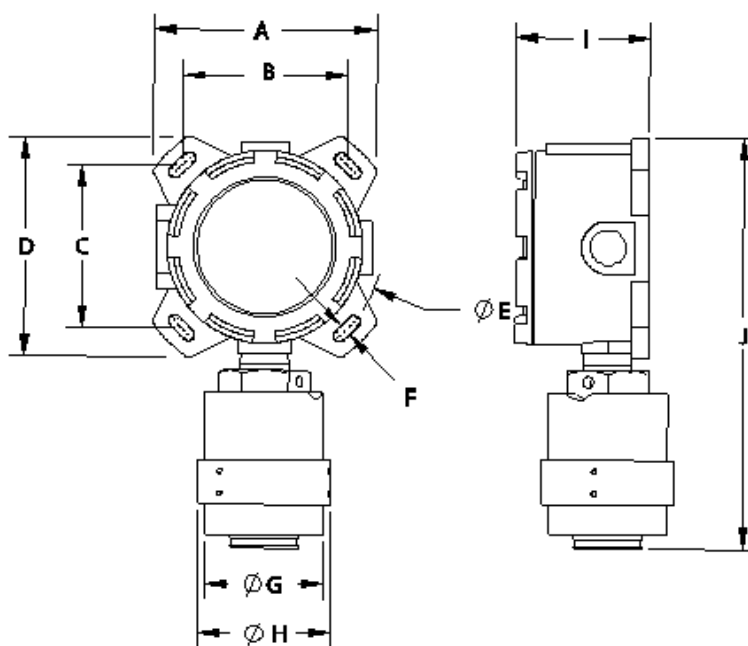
Габаритные размеры корпуса и сенсора Net Safety Millennium II Basic (M2B) или распределительной коробки (РК)
